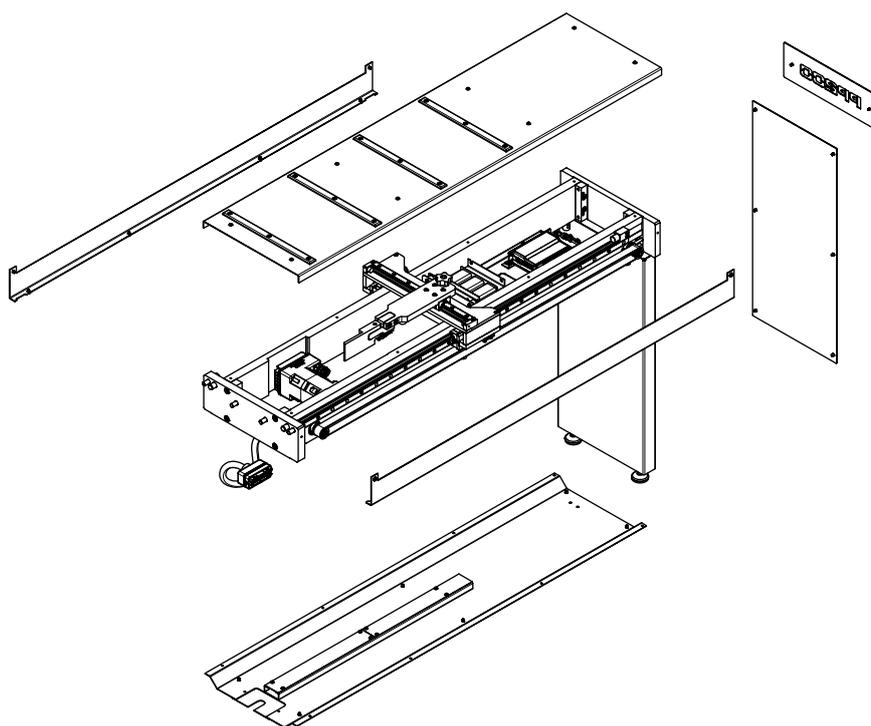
Vue éclatée des capots de la butée pour la presse horizontale PP200CNC
